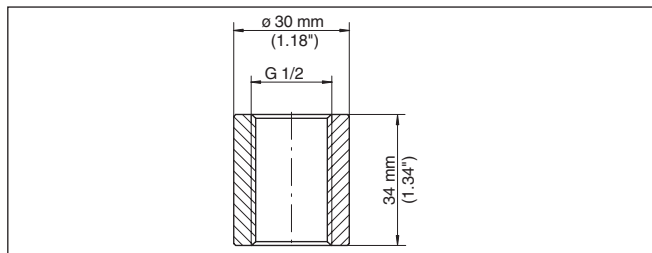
Dimensiones racor soldado rosca G $\frac{1}{2}$ (EN 837) - conexión de manómetro
